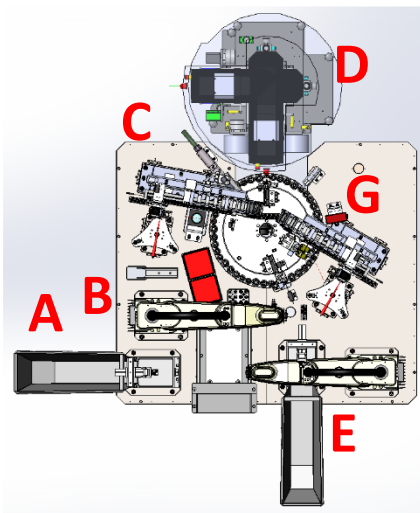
Vue de dessus de la machine d'assemblage corps - douille
